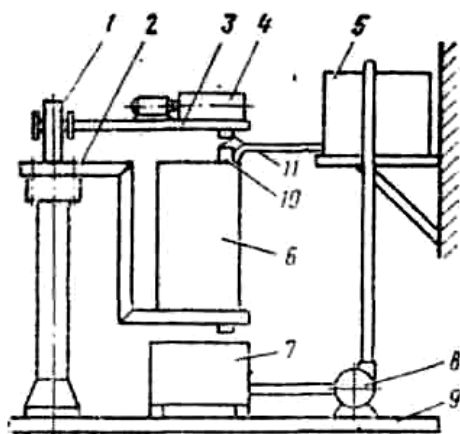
Схема установки для восстановления постелей коренных подшипников блока цилиндров двигателя электронатирием:
